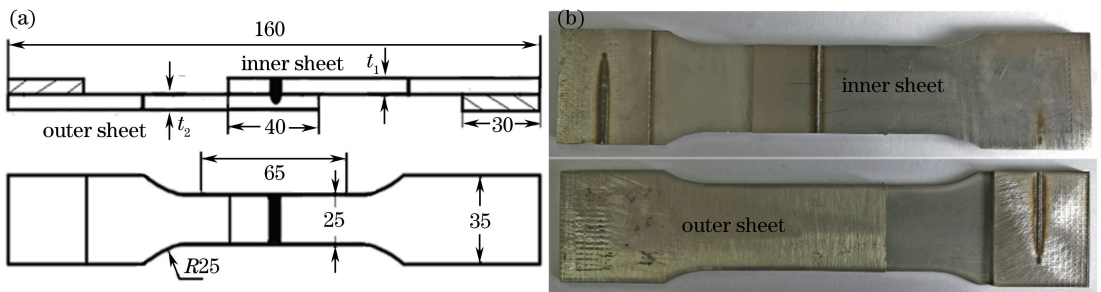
搭接激光焊接拉伸试样。(a) 尺寸; (b) 实物
